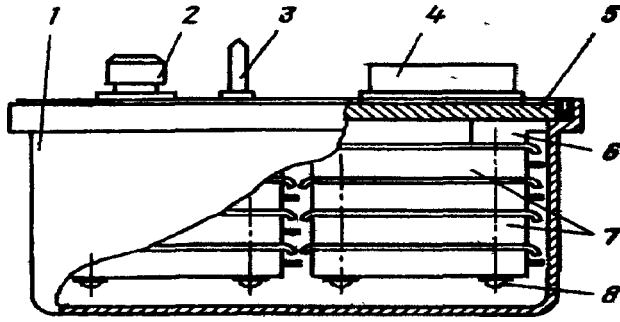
Этажерочная конструкция блока приемопередающего устройства IV поколения: 1 — кожух; 2 — высокочастотный разъем с полиэтиленовой заглушкой, 3 — трубка-шгенгель; 4 — низкочастотный разъем; 5 — крышка-основание; 6 — бобышка; 7 — субблоки; 8 — стяжной винт
